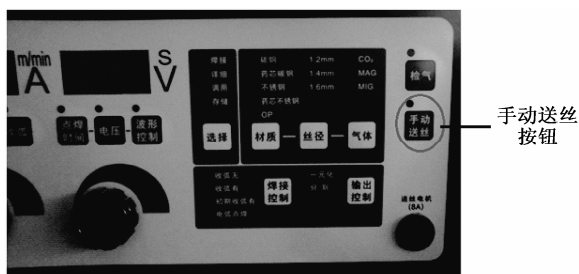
焊接电源面板及手动送丝按钮位置
